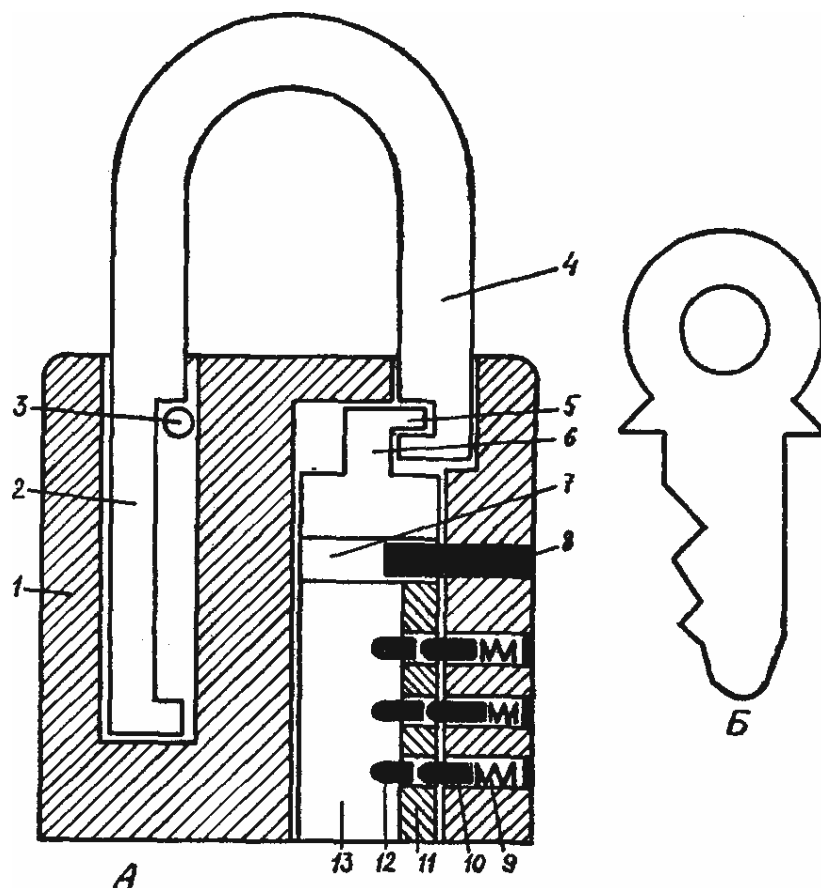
Устройство навесного цилиндрического замка с литым корпусом:
